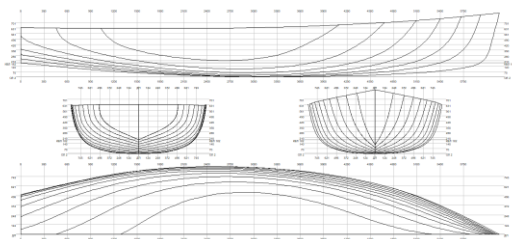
Теоретический чертёж (ТЧ) шлюпки
